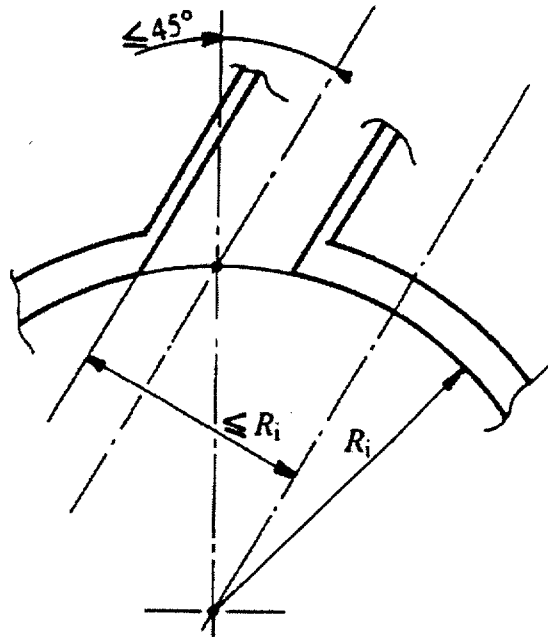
Tubulure soudée obliquement sur une enveloppe sphérique ou un fond bombé.
